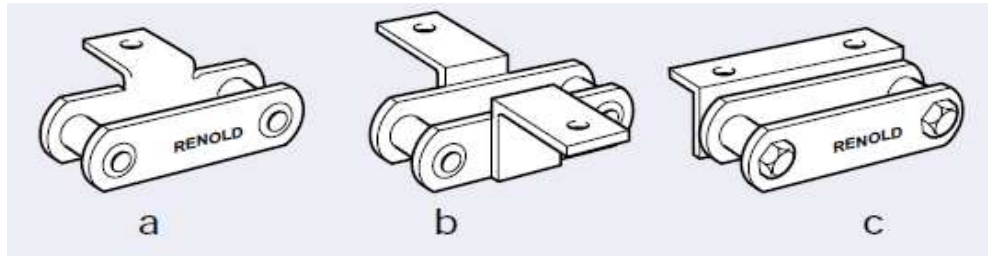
Accesorios tipo K. a) K1, accesorio doblado, b) K1, soldados a la placa de unión y c) K2, atornillado a través del pasador hueco.
